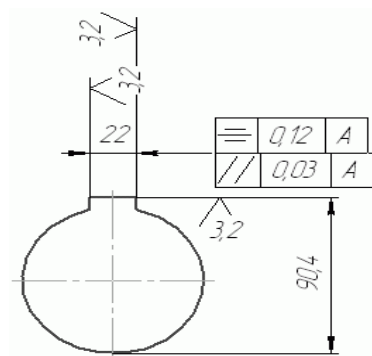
Размеры, шероховатость и допуски профиля отверстия в ступице колеса
